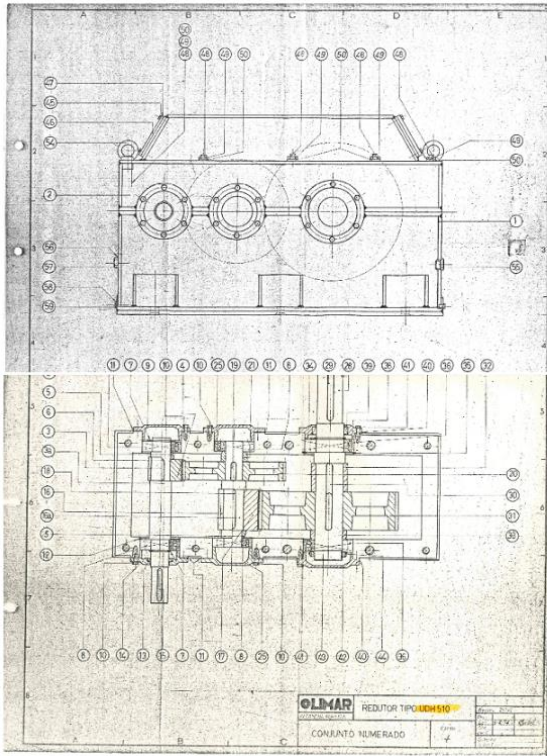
Desenho técnico do Redutor Olimar UDH 510
